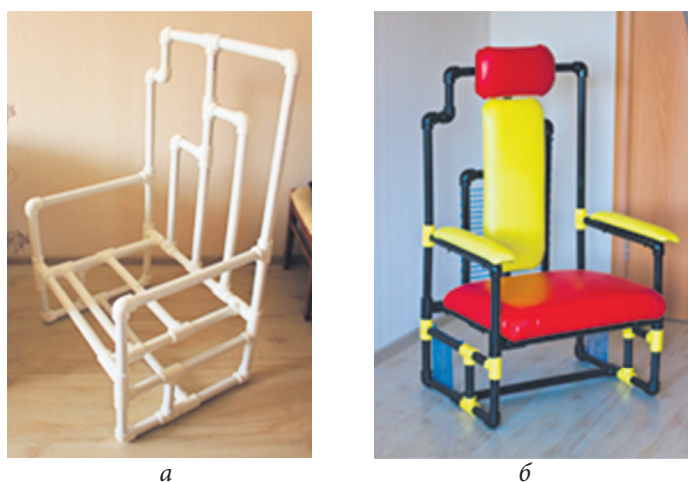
Изготовление опытного образца изделия из труб ПВХ: а — каркас кресла из труб ПВХ; б — опытный образец кресла
